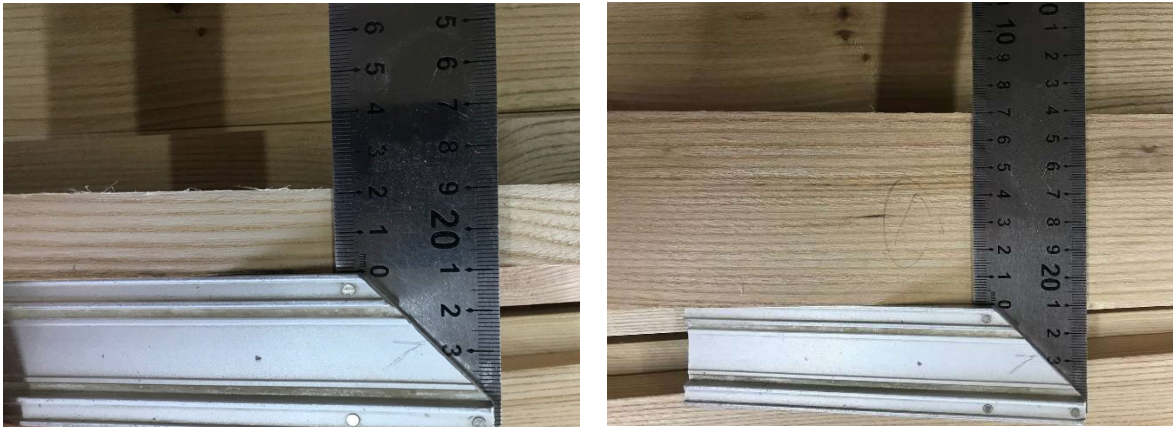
Заміри товщини та ширини отриманої заготовки
